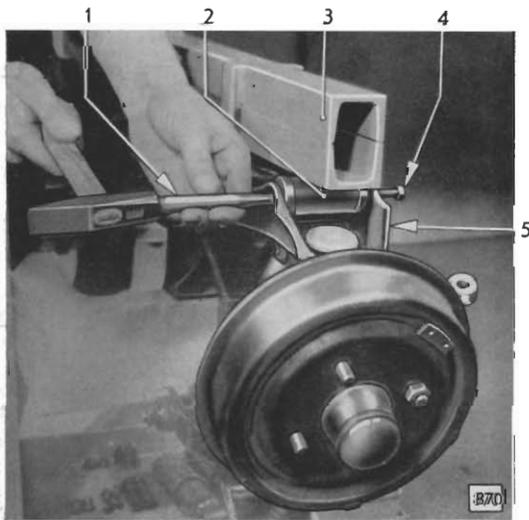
Sechskantschraube mit Dorn herausschlagen
